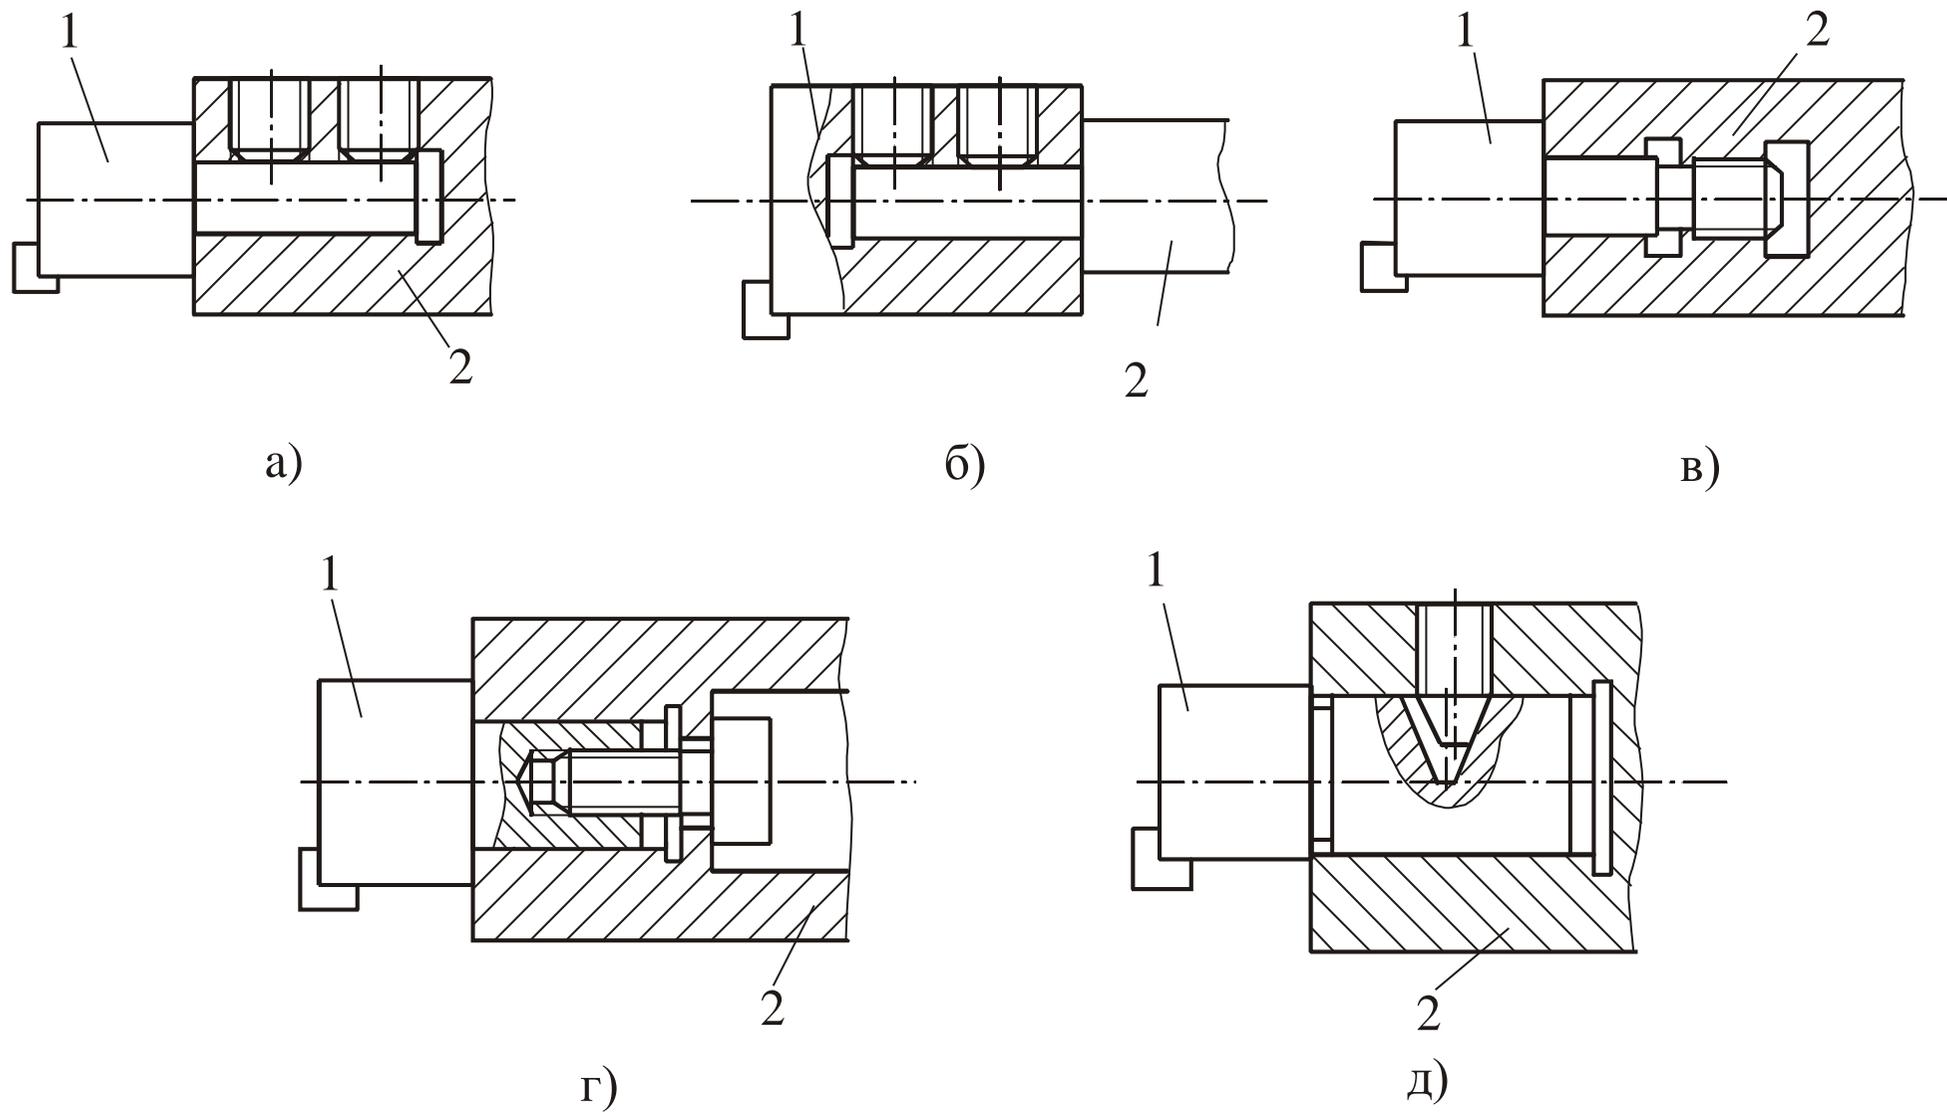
Схемы соединений сменного инструмента: 1 – инструмент; 2 – оправка
